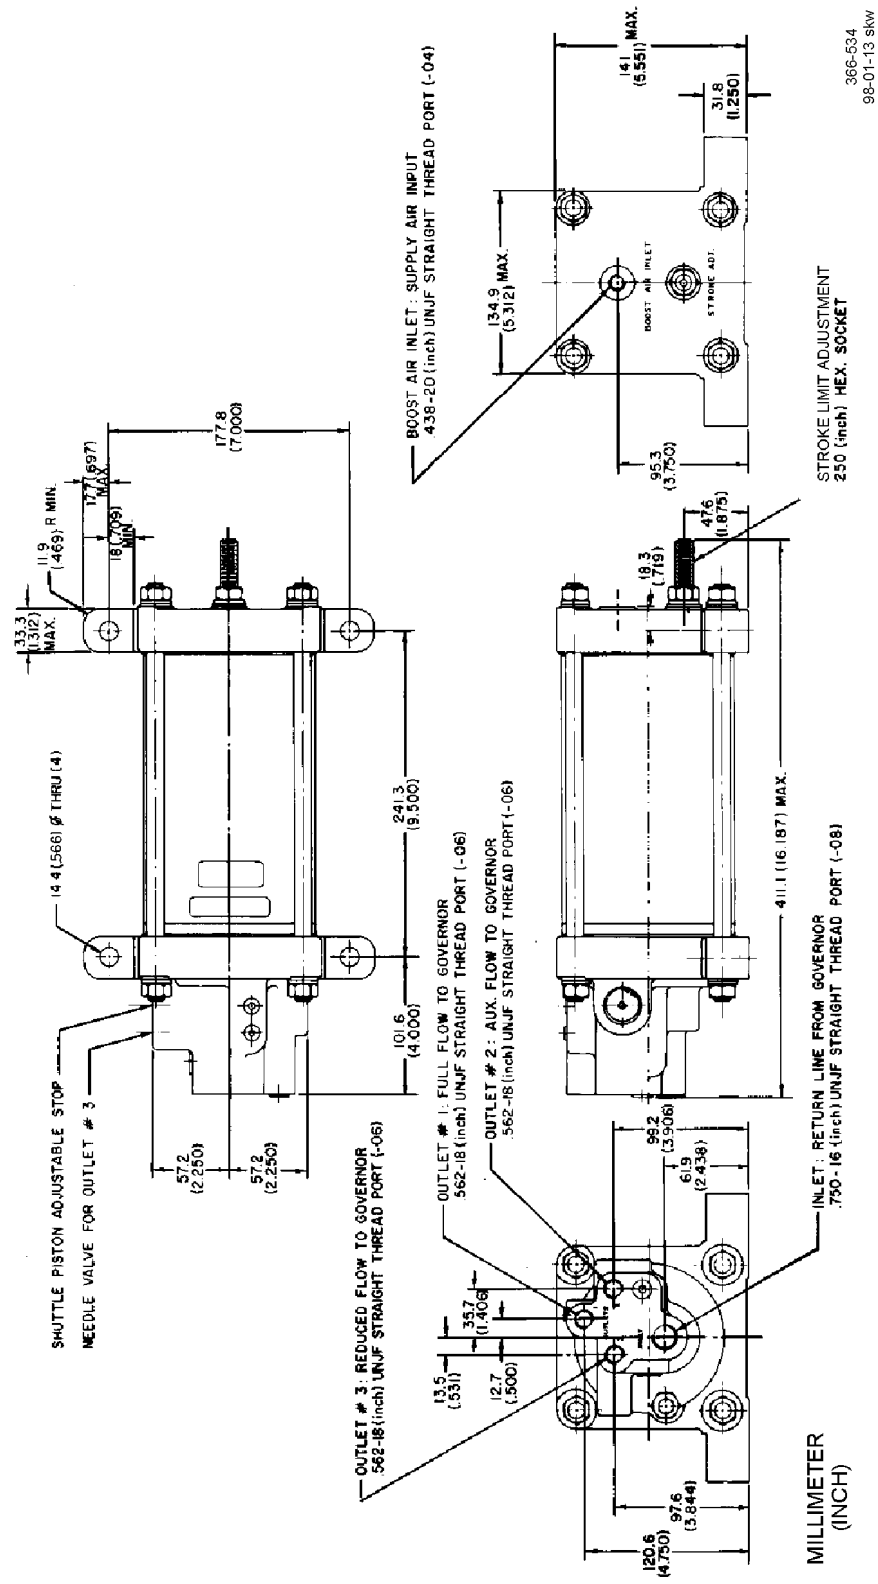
Габаритный чертёж двухступенчатого бустера
